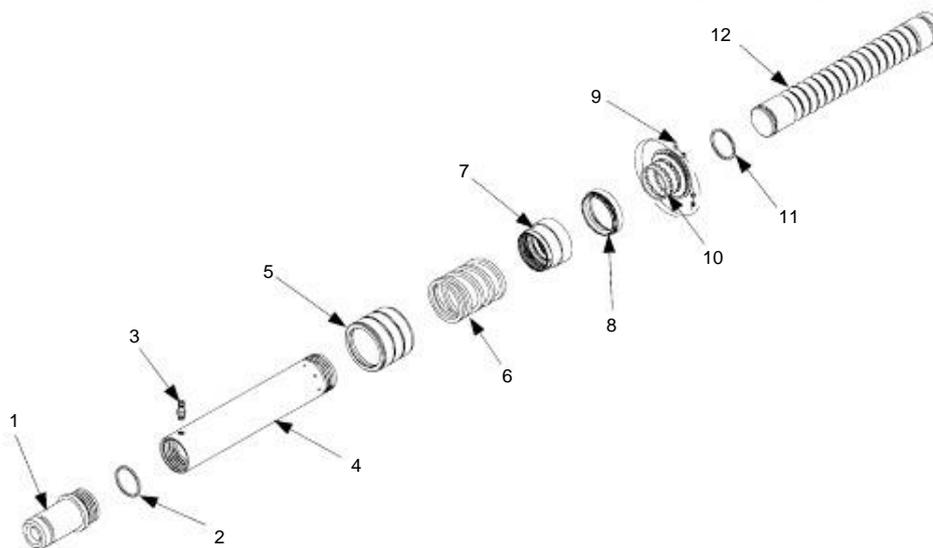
Lockstroke-Stütze, Explosionszeichnung
